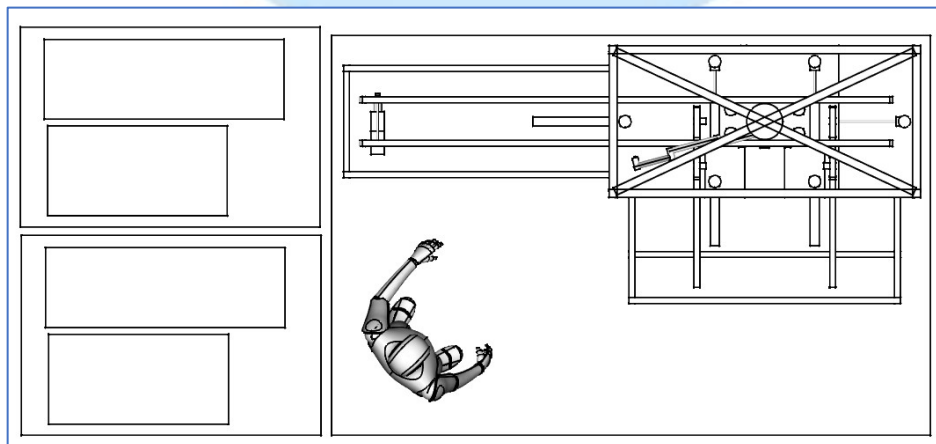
Solusi sistem automasi sistem, tampak Isometric
